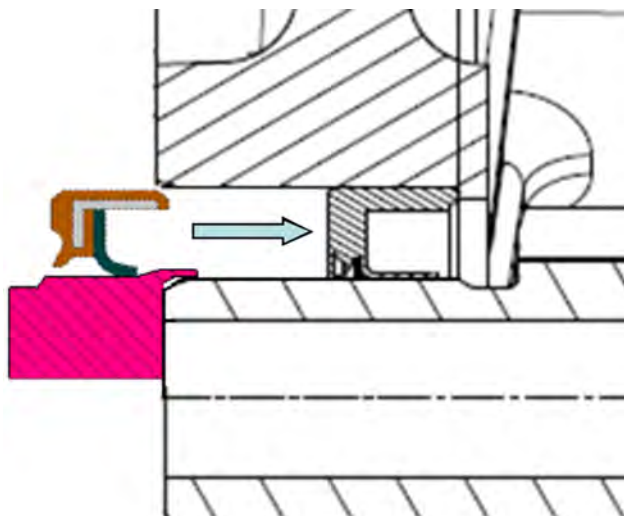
Montage de la bague d'étanchéité sur le vilebrequin à l'aide d'une broche de montage
